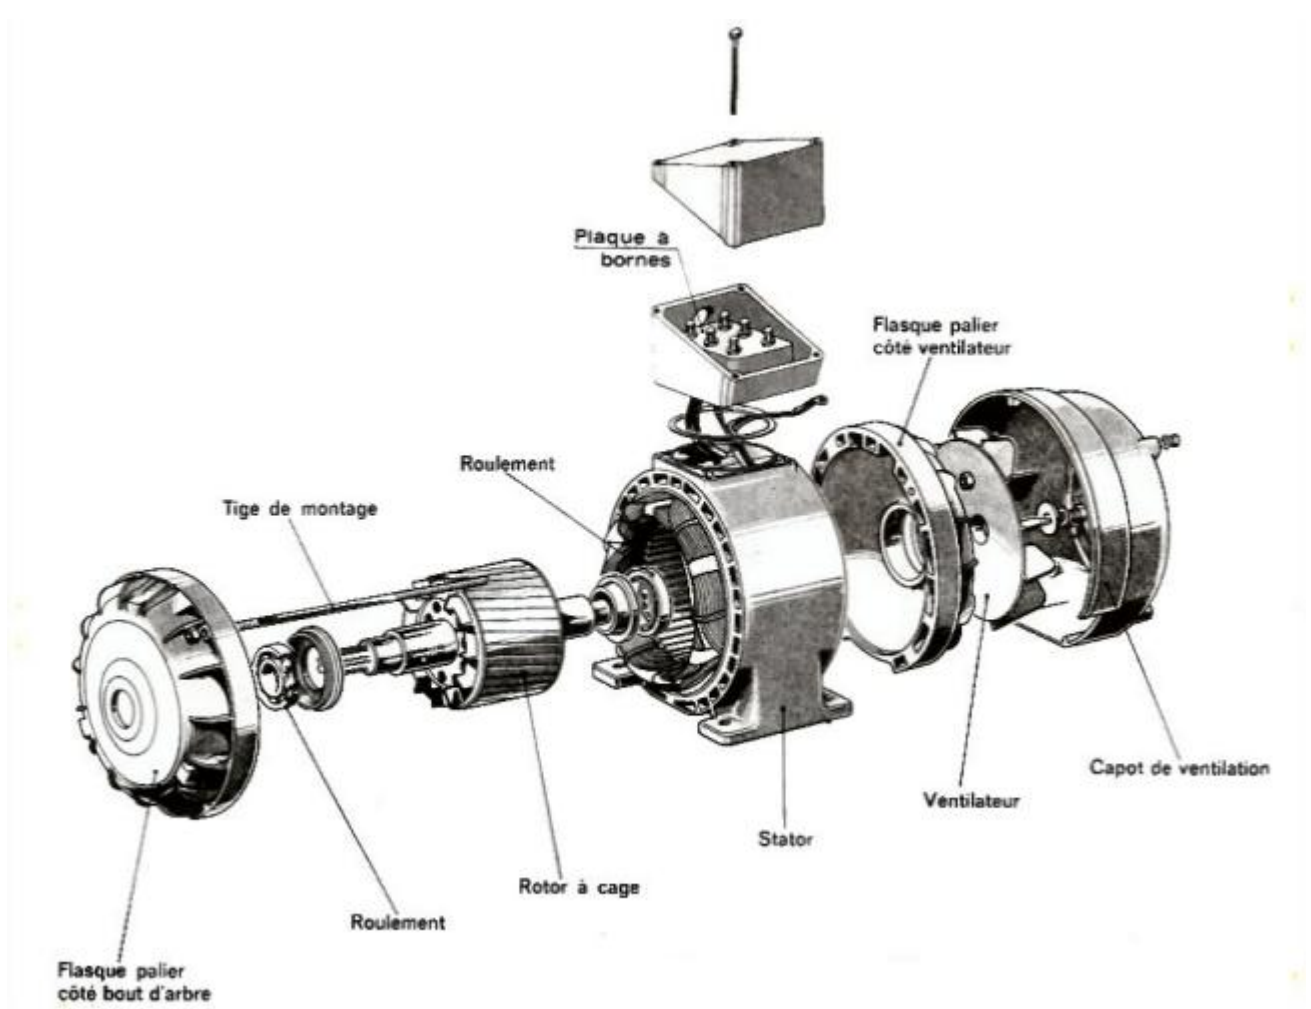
Vue éclatée d'un moteur asynchrone à cage
